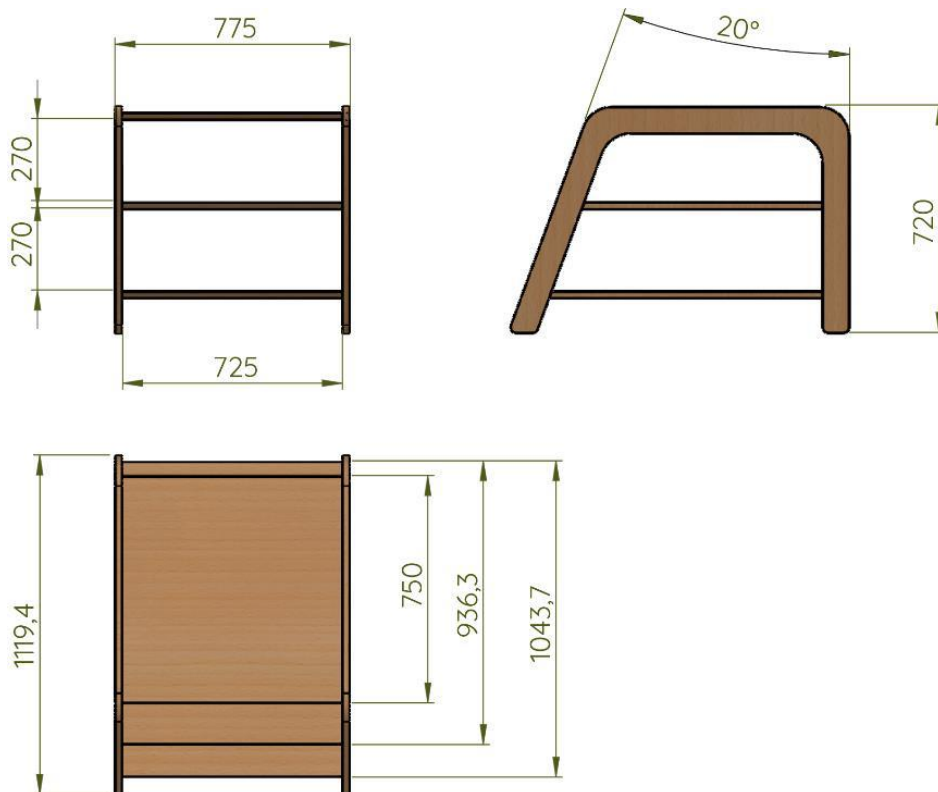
Dimensionamento geral do vaso de plantas em mm
